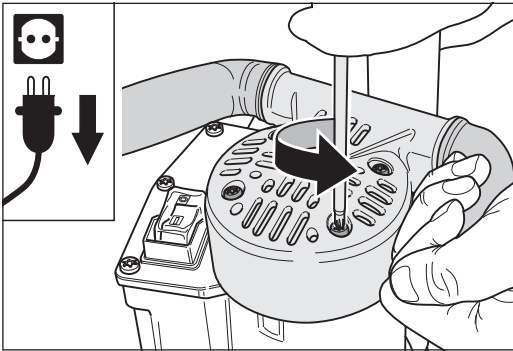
Die vier Befestigungsschrauben des Griffstücks entfernen.
